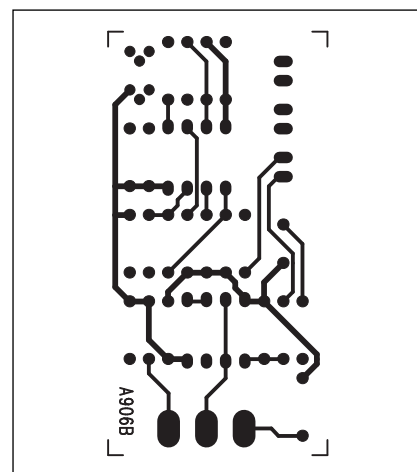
Obrazec desky spojů čidla (strana TOP)
